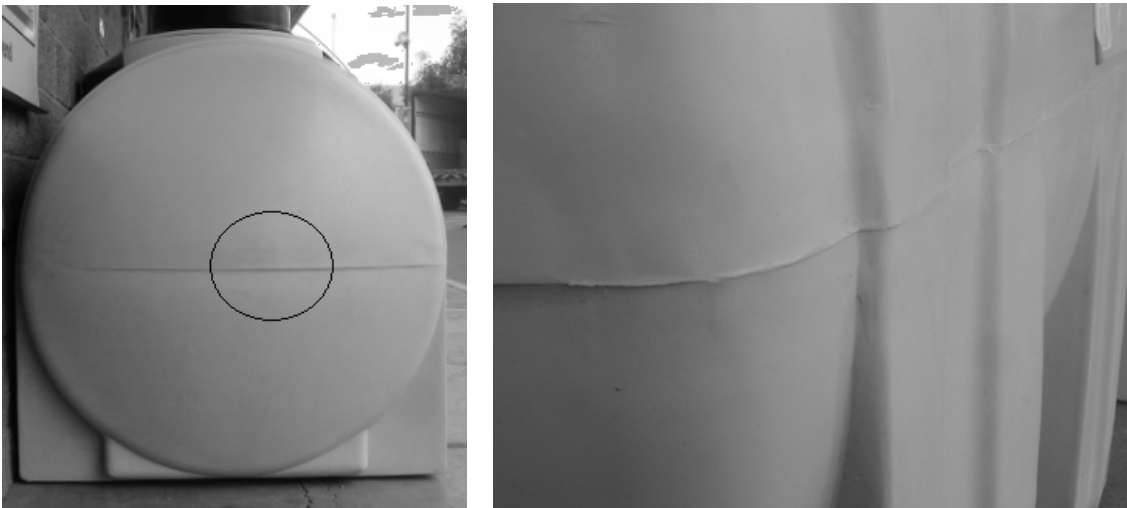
Defectos en la línea de unión, defasamiento del molde y producción de rebaba.
